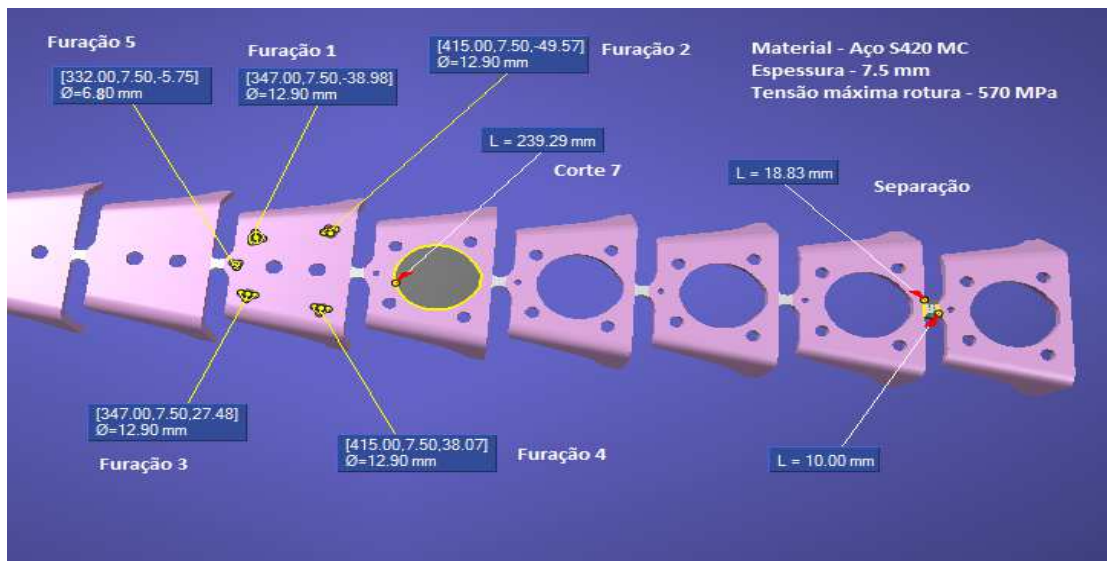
Estampagem do suporte de roda, após dobragem do produto.
